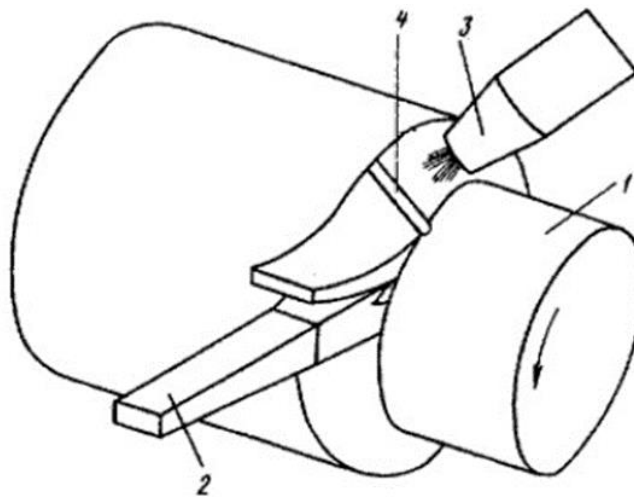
Способ механической обработки с подогревом, где 1 – обрабатываемая заготовка, 2 – режущий инструмент, 3 – плазмотрон, 4 – стружкоразделительная канавка [57-59]
